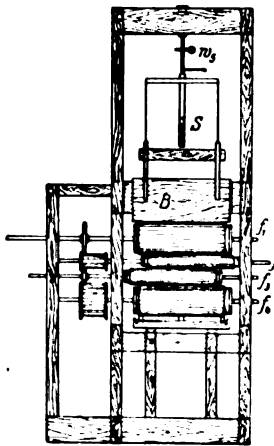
Farbwerk der Suhler Maschine, Seitenansicht
